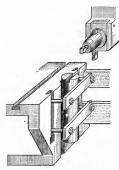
Крепление заготовки на боковой поверхности стола поперечно-строгального
